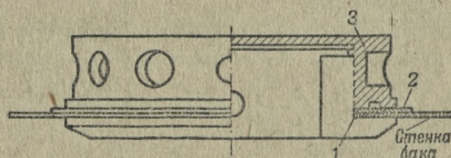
Пробка Фирсова для быстрой заделки пробоин
